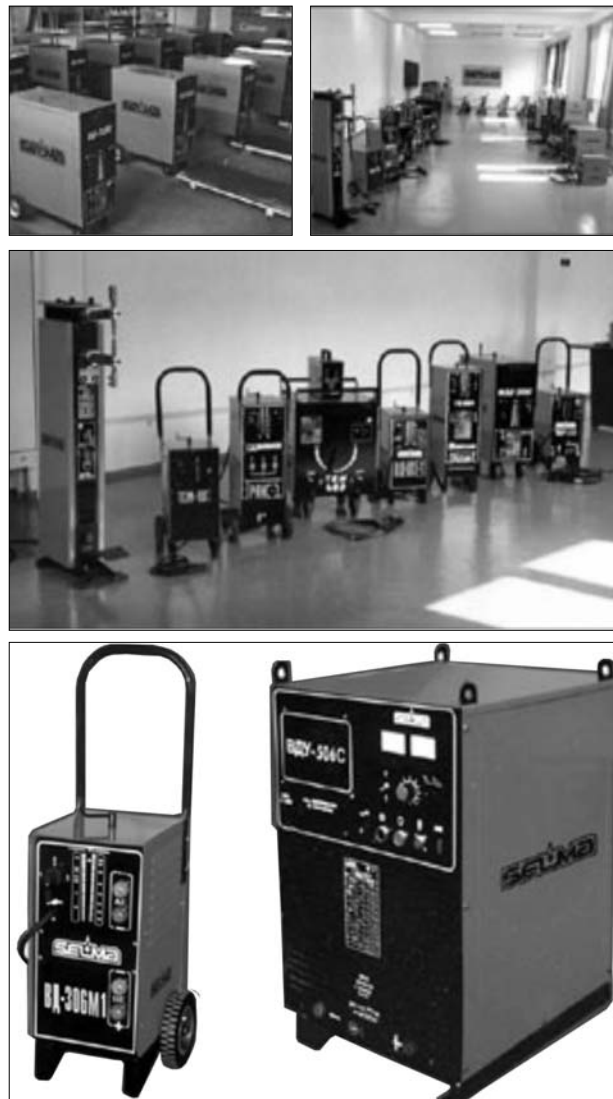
Современное оборудование для дуговой и плазменной сварки
